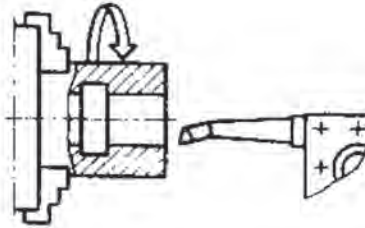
Попередня обробка торця та отвору перед нарізанням різьби
